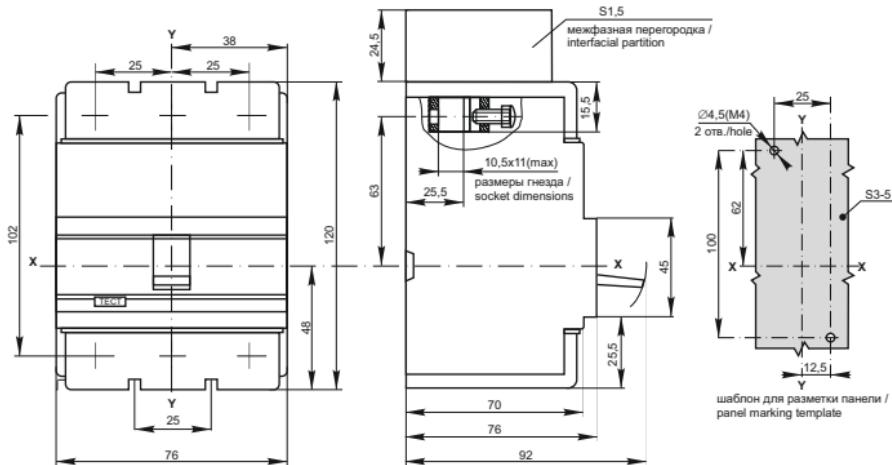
Габаритные и установочные размеры выключателя ВА88-32 /
